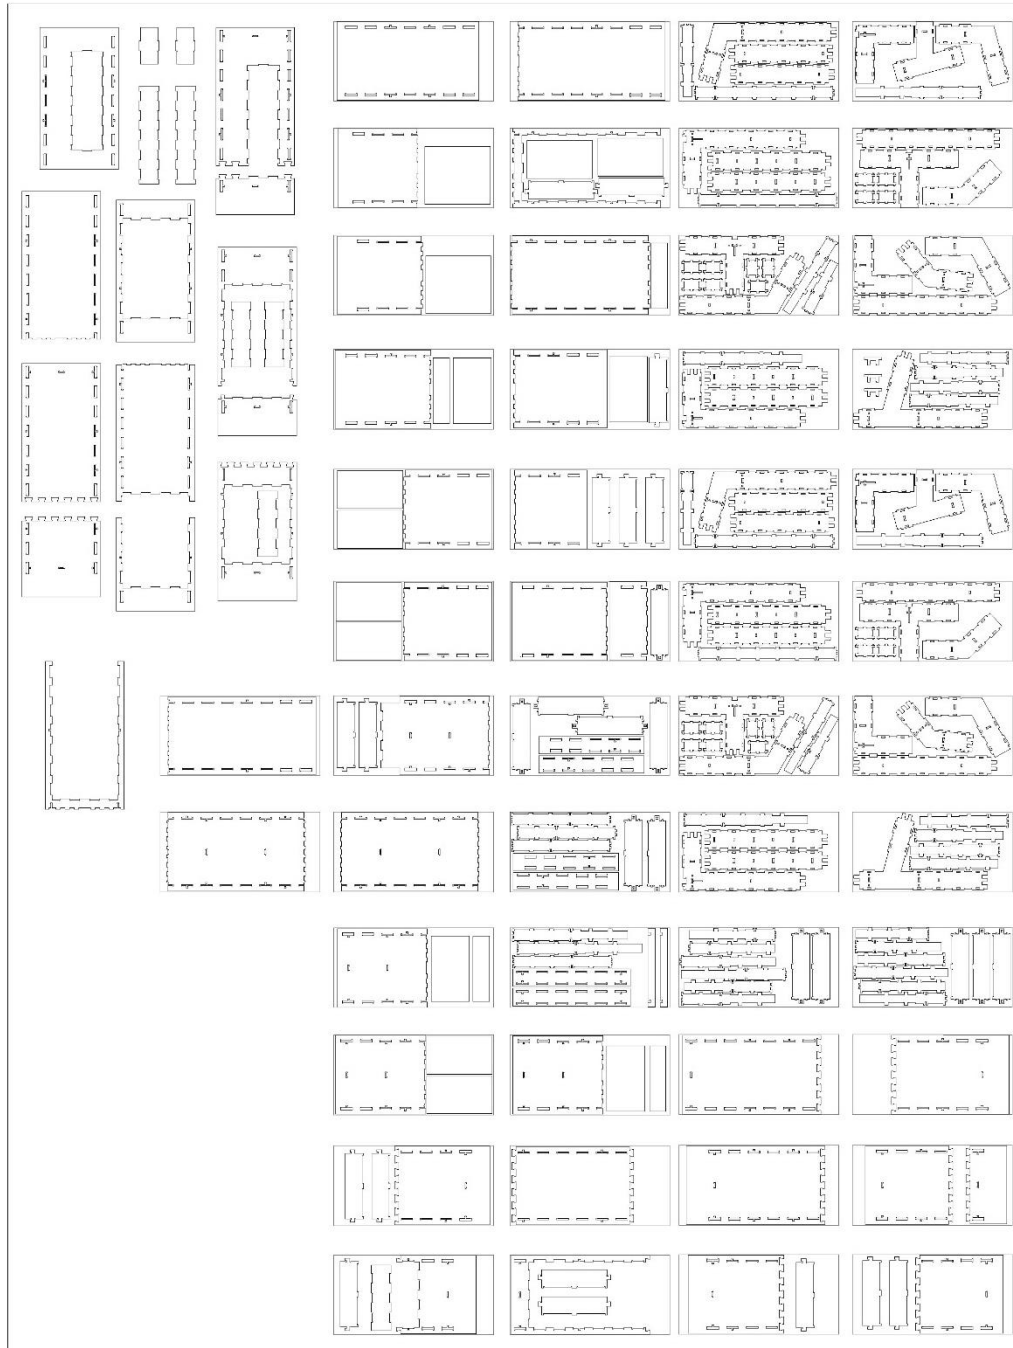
Ensamble de piezas para crear un pórtico estructural
